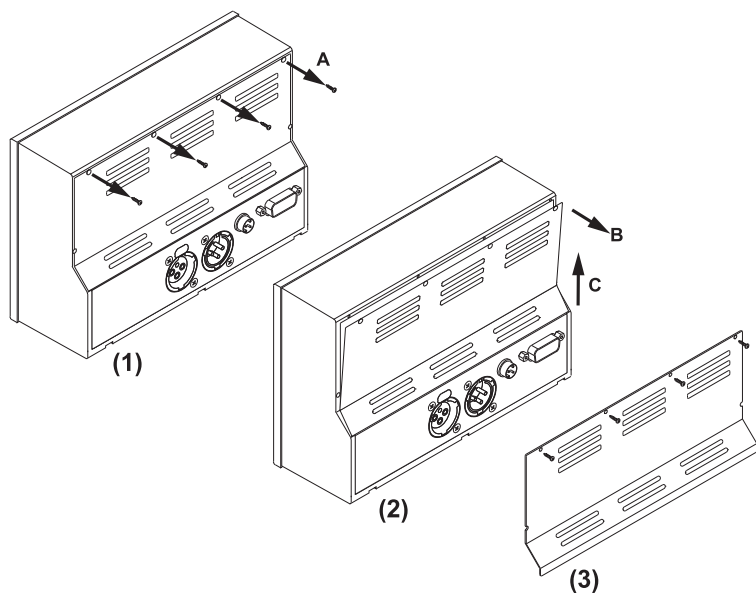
Entfernen des rückwärtigen Abdeckblechs
